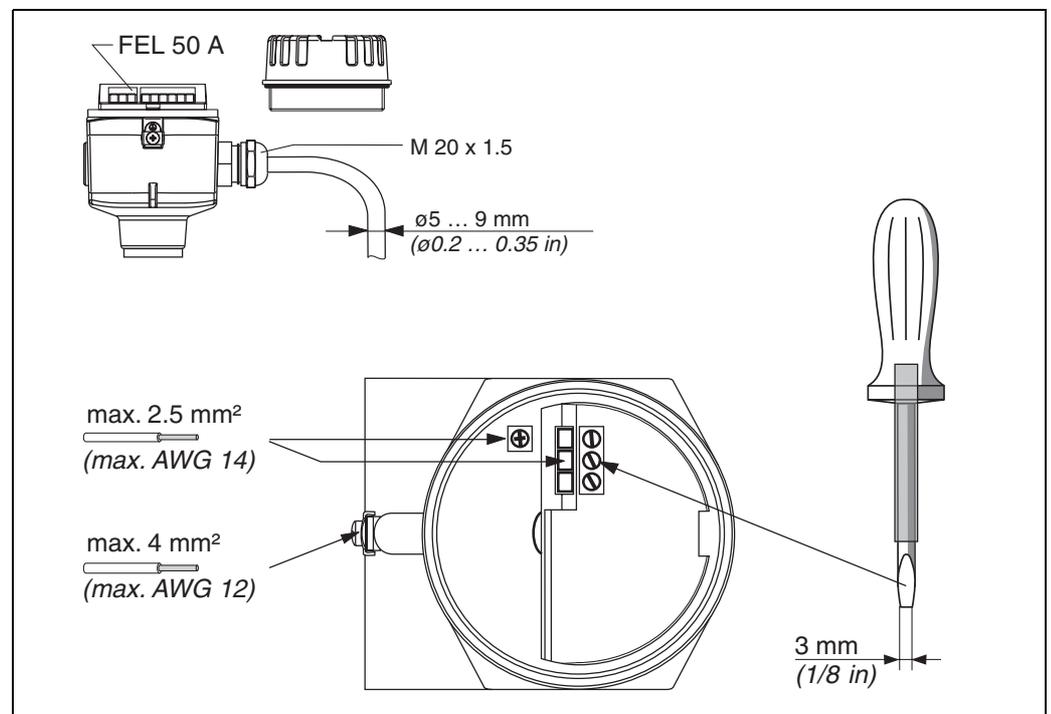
Anschließen des Messumformers mit Kabelverschraubung
